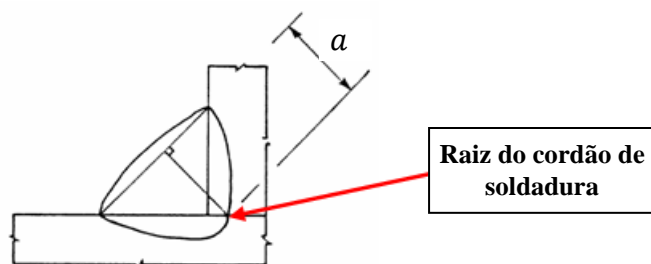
Espessura de um cordão de soldadura com elevada penetração.
